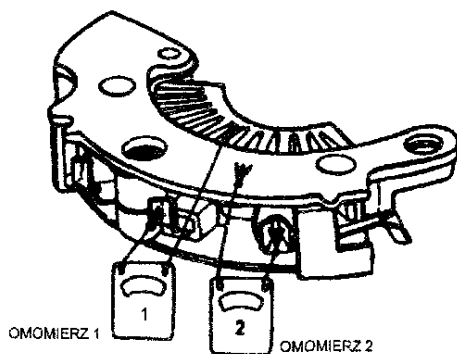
Alternator CS 130: demontaż, sprawdzenie, montaż
